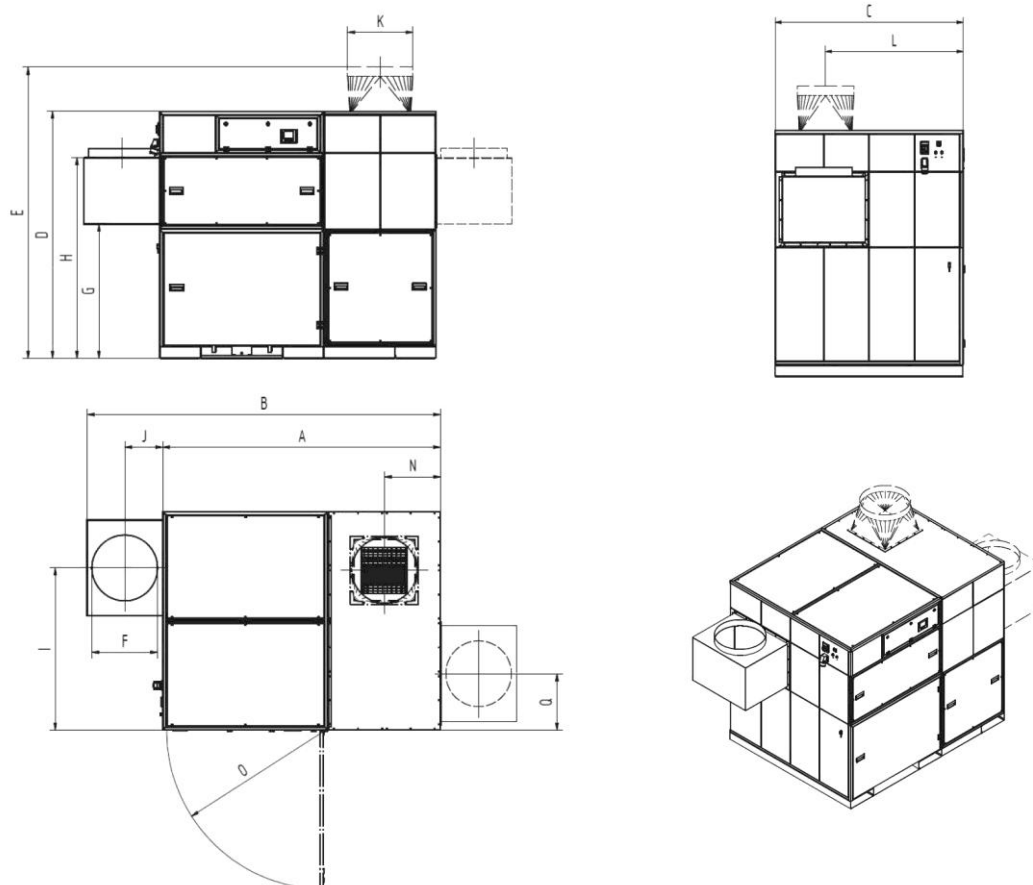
Габаритный чертеж 3250110, 3250112, 3265111, 3265112
